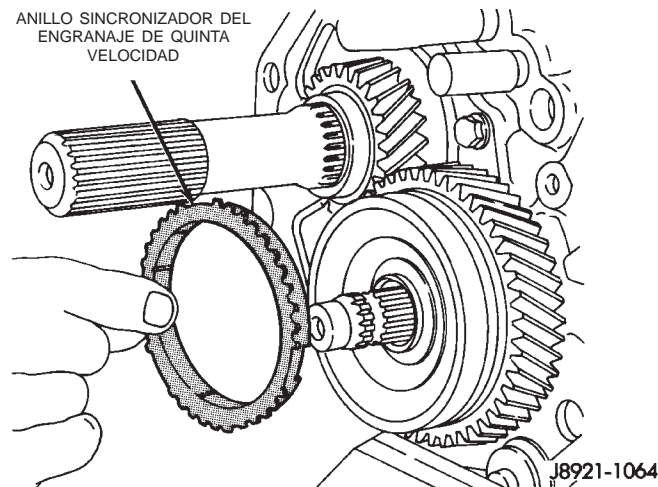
Desmontaje del anillo sincronizador del engranaje de quinta velocidad
